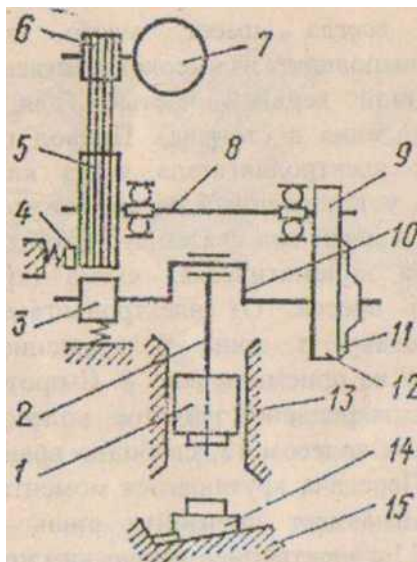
Кинематическая схема кривошипного горячештамповочного пресса
